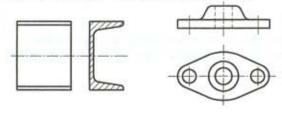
6 Přerušení obrazu: souvislou tenkou čarou se zlomem - obr. a), b), nebo c)
